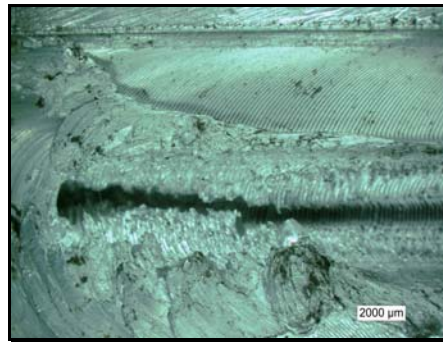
Welded surface after tangential removal of the tool
